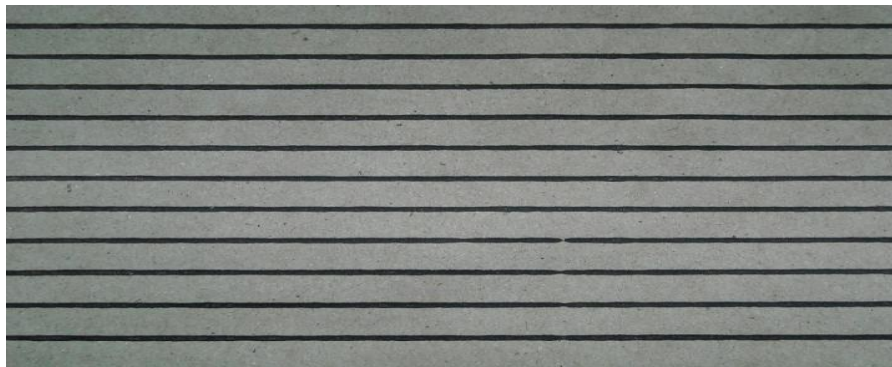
Dépôt de colle régulier sur toute la laize du carton
